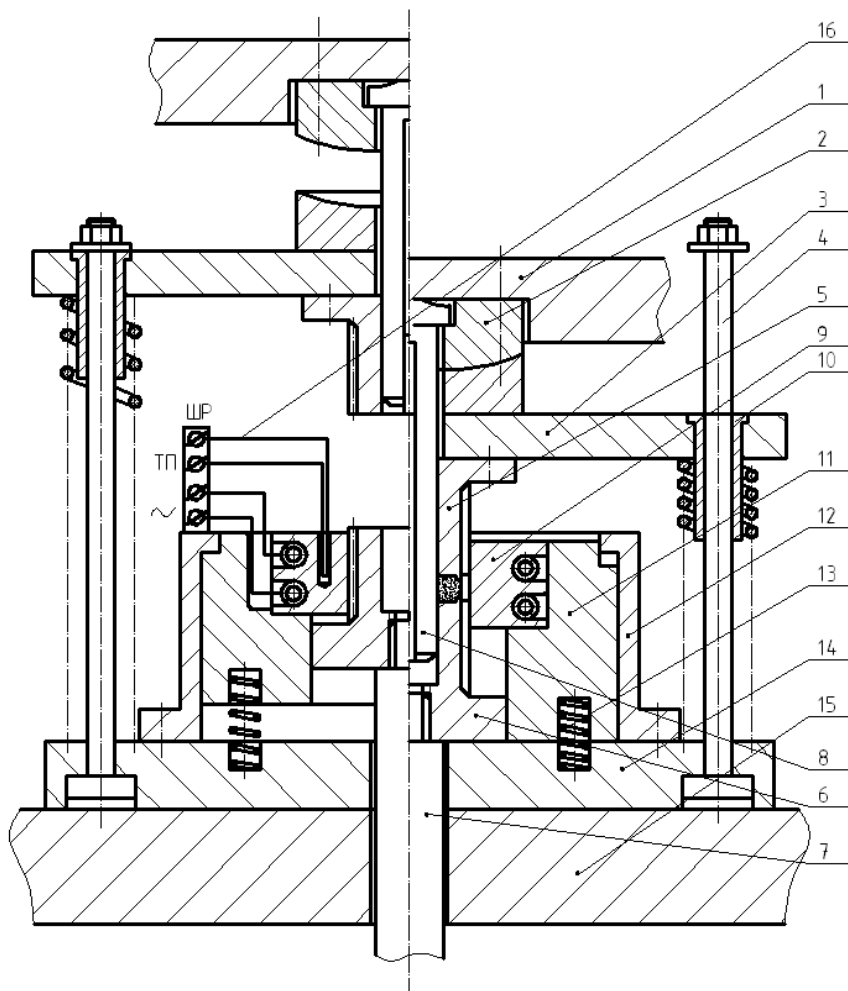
Схема блока для горячей штамповки изделий из пористых порошковых заготовок
